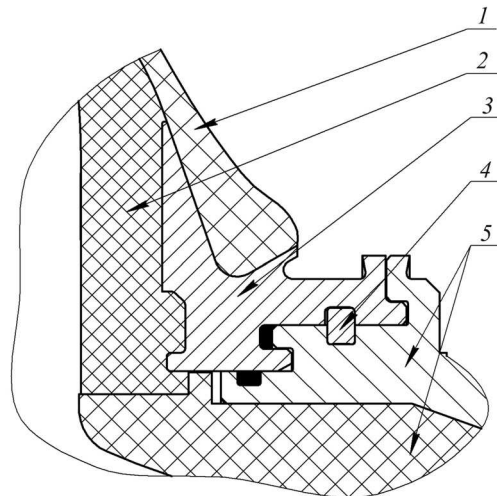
Соединение корпуса типа «кокон» с соплом: 1 – пластиковое днище; 2 – теплозащитное покрытие корпуса; 3 – закладной фланец корпуса; 4 – шпонка; 5 – стыковочный шпангоут сопла с теплозащитным покрытием
